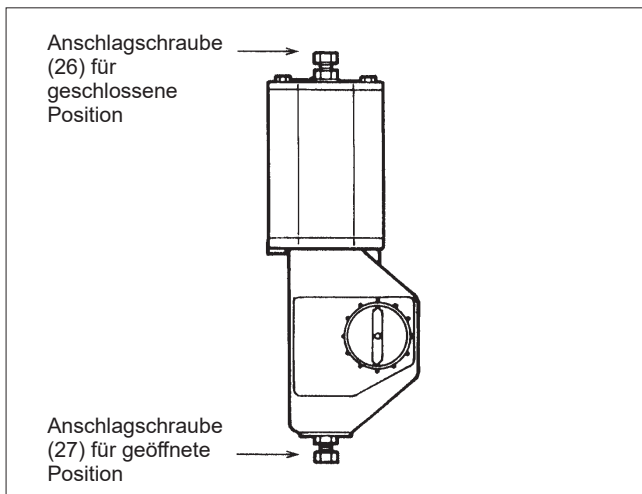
Die Anschlagsschrauben in geöffneter und geschlossener Position
